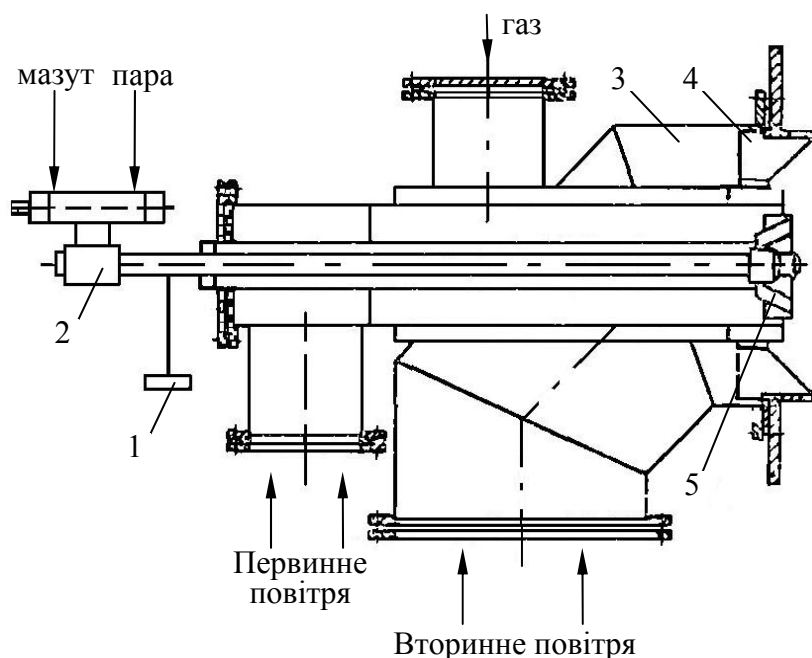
Конструкція газомазутного пальника: 1 – заглушка; 2 – форсунка; 3 – повітряна частина; 4, 5 – лопаткові завихрювачі; 6 – монтажна плита
